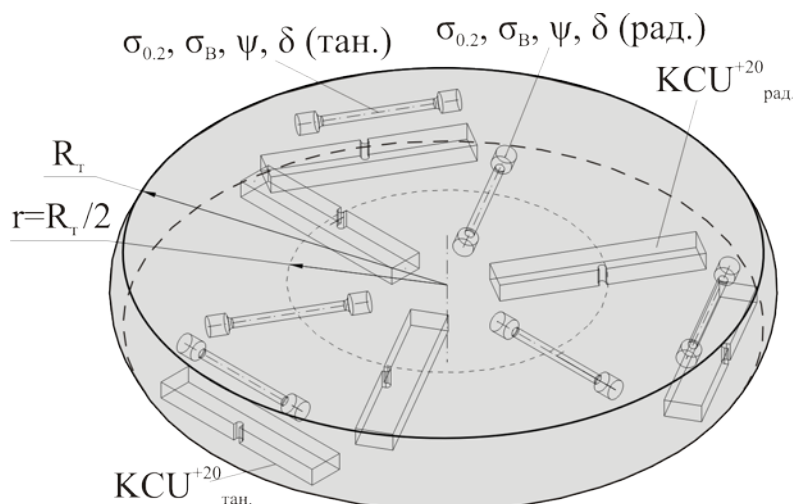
Схема вырезки образцов для механических испытаний из кованой заготовки
